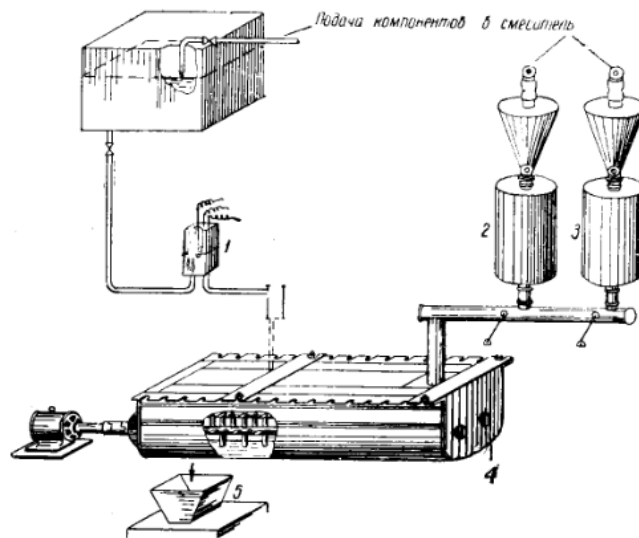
Шнековий змішувач для приготування пасти:
